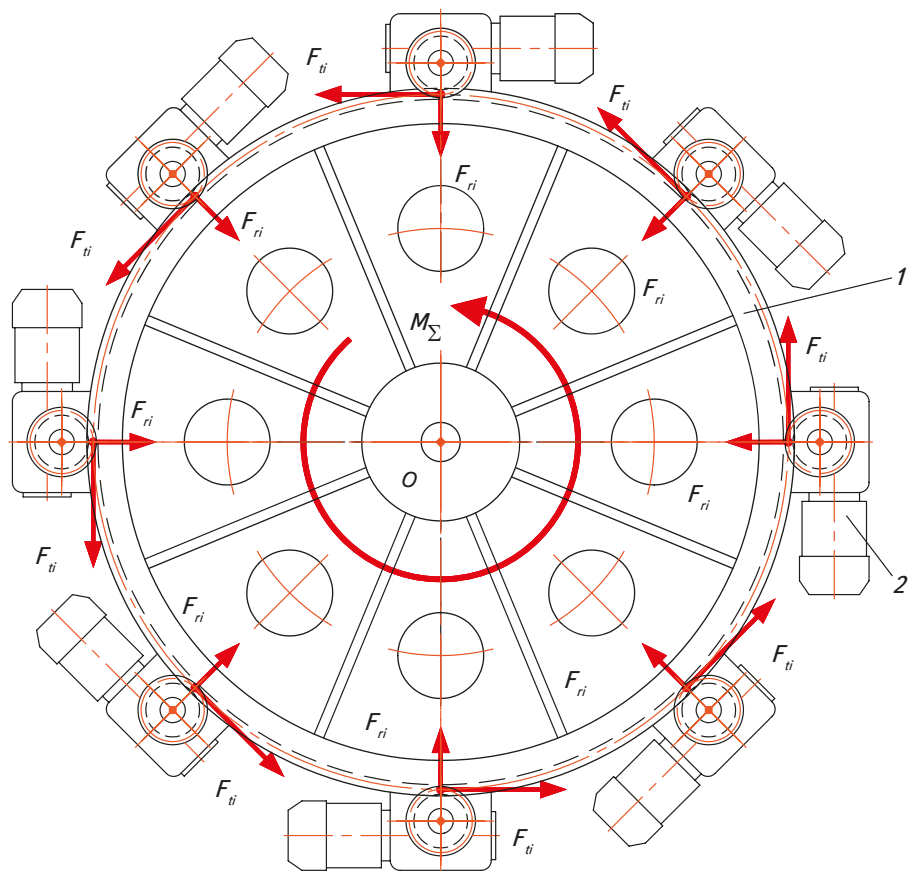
Схема привода трубовала колонного диффузионного аппарата: зубчатое колесо трубовала; 2 – мотор-редуктор с шестернёй
